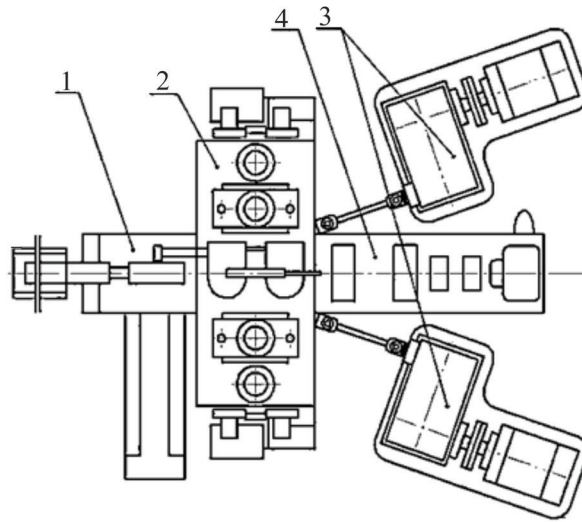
Схема расположения оборудования прошивного стана с индивидуальным приводом валков:
